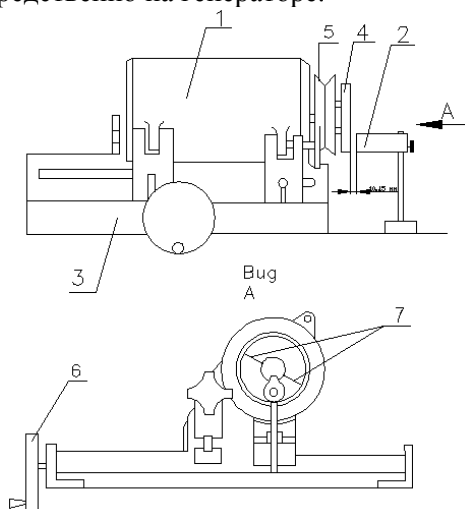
Внешний вид стэнда 532-2М для проверки генераторных установок
